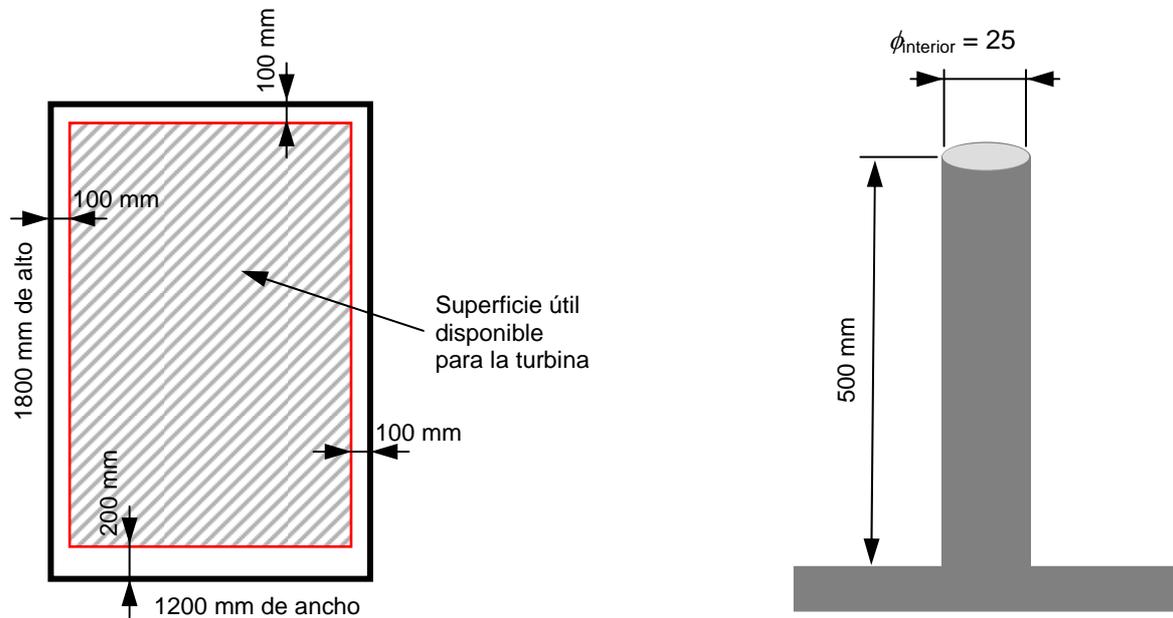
Izquierda: sección neta utilizable del túnel de viento. Derecha: tubo hueco para sujeción del eje.
